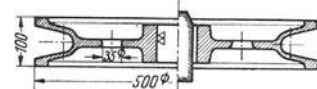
Seilrolle (Werkzeichnung und Werkaufriß).
